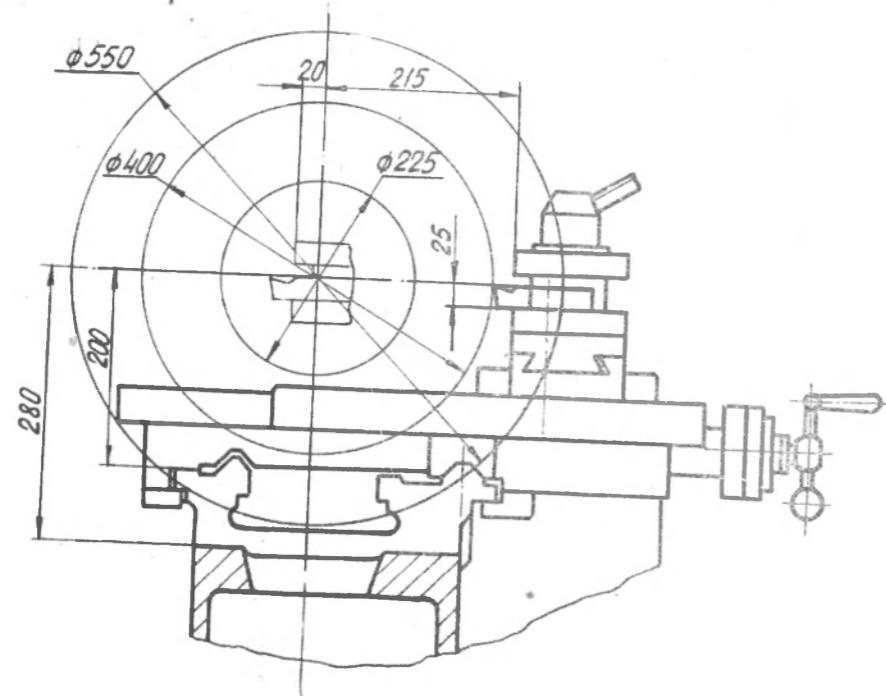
Суппорт — габаритные размеры рабочего пространства станка.
